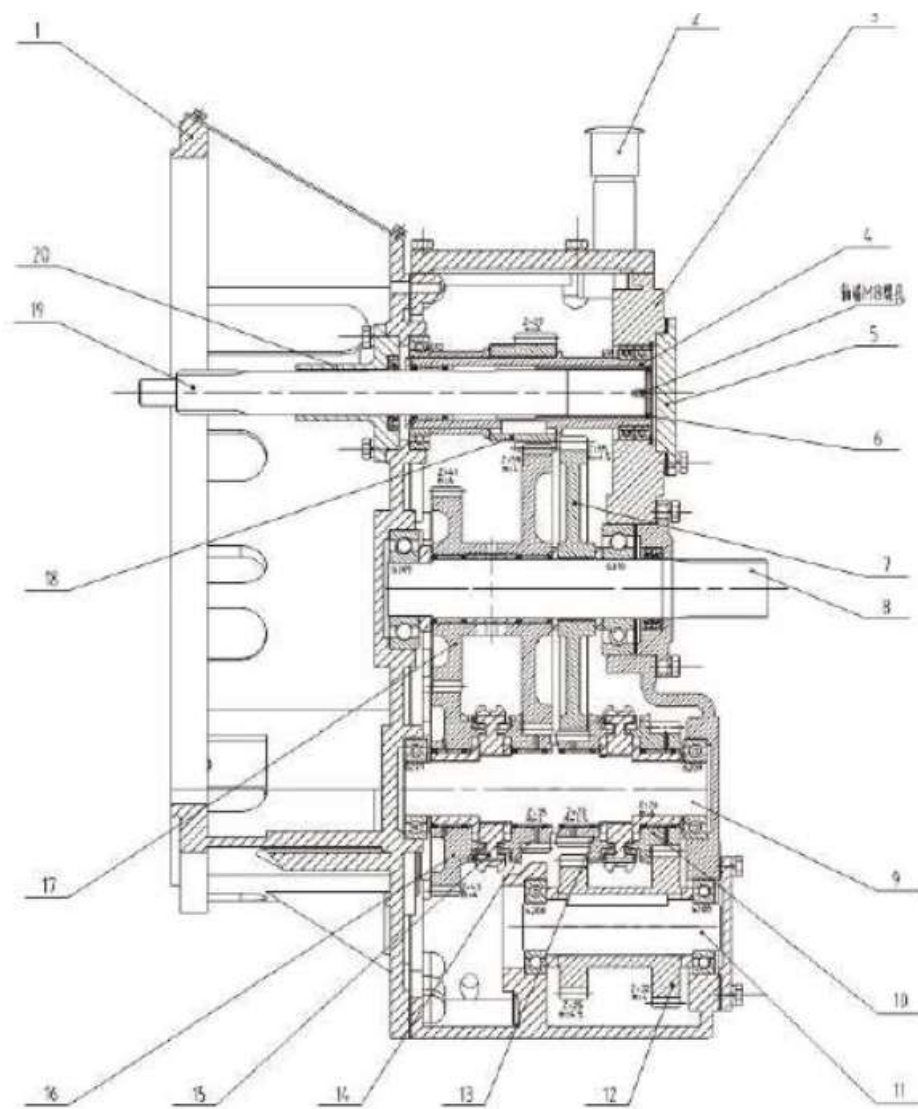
В. Коробка передач с двумя рычагами:
